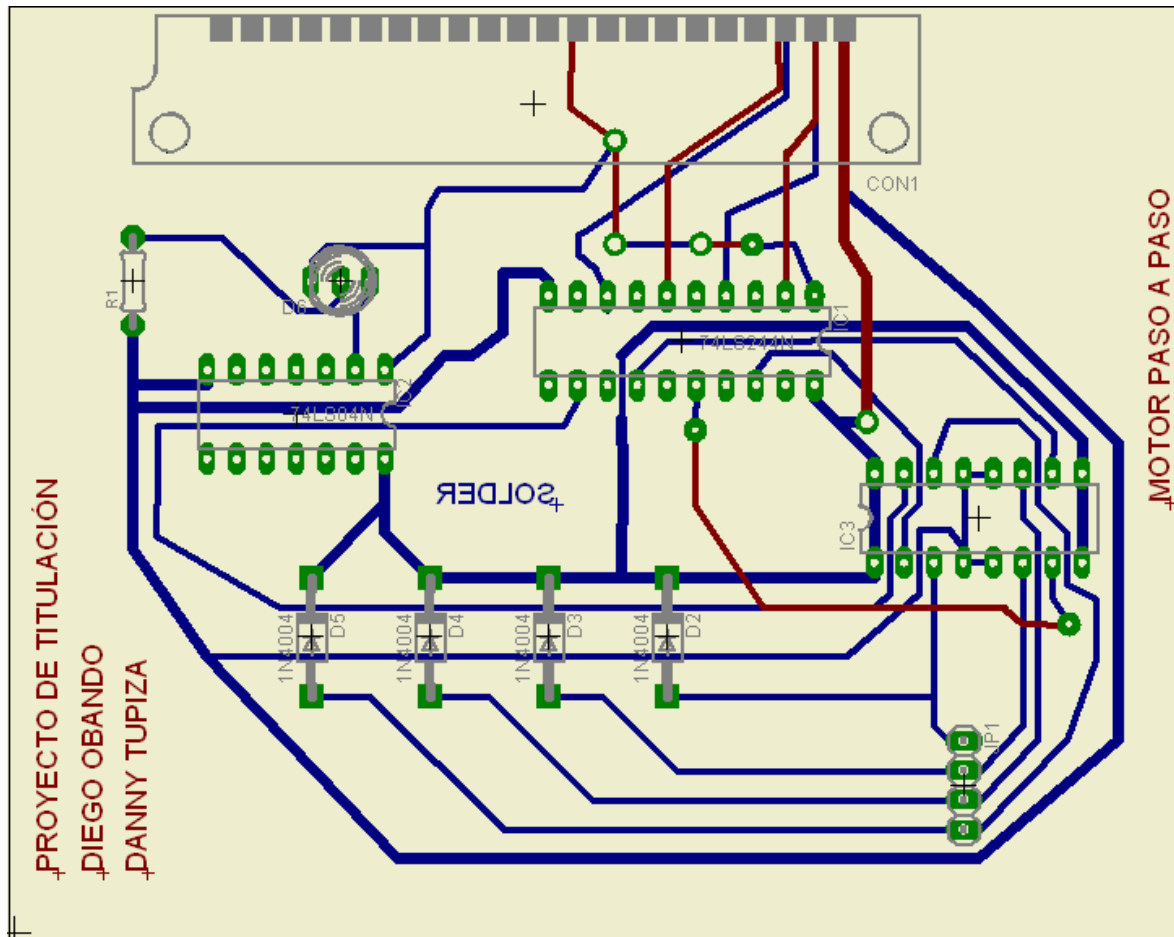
Diagrama board de la tarjeta motor paso a paso
